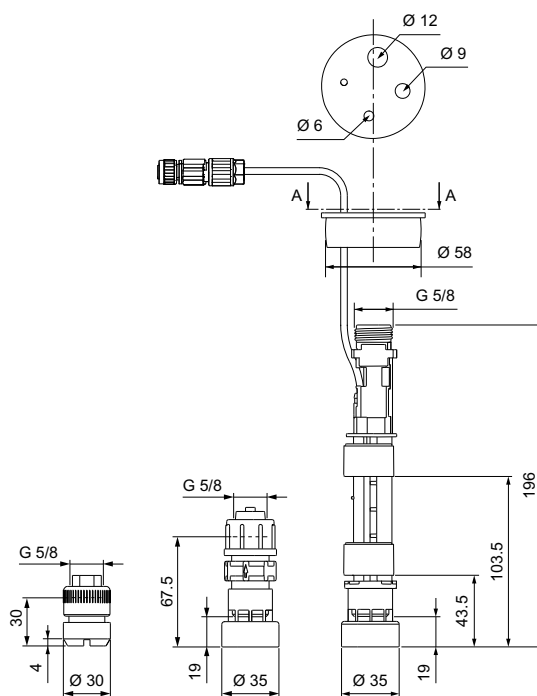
Vänster: bottenventil av rostfritt stål, mitten och höger: bottenventil av PE eller PVDF, mått
